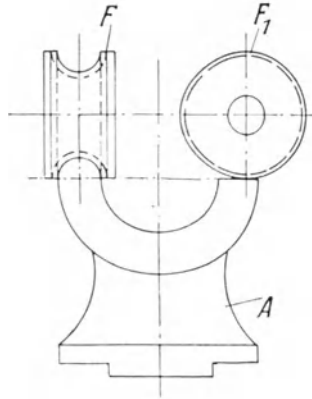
Fräsen der Fläche und des Radius am Verschluß- und Scharnierteil.
